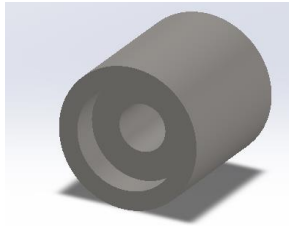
Vista detalle de soldado de pieza N°7 (Fuente 95)
